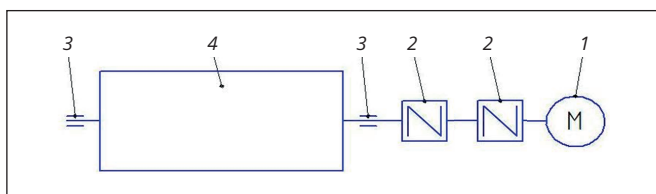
Кинематическая схема привода шаровой мельницы после модернизации: 1 – мотор-редуктор; 2 – муфты зубчатые; 3 – подшипниковые узлы; 4 – мельница
